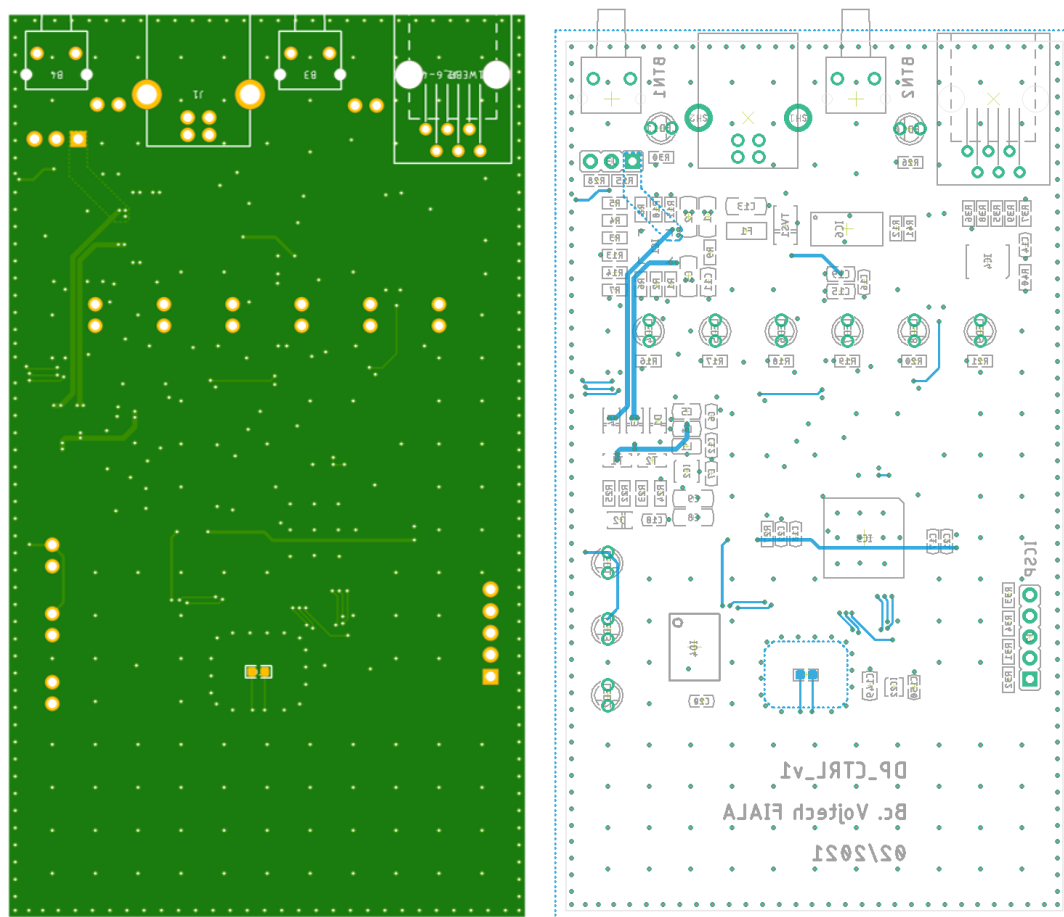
Náhled a layout horní (top) strany plantární DPS
